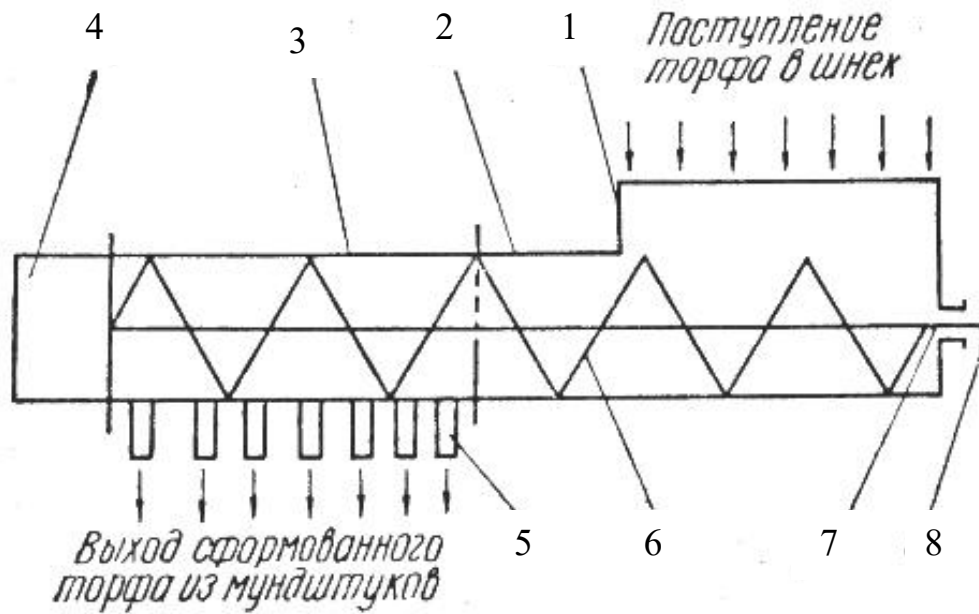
Шнековый пресс конструкции Ф.А. Опейко:
